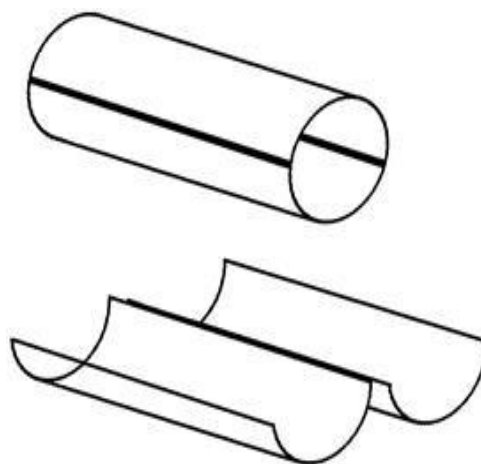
Циліндрична обичайка с двома поздовжніми швами
